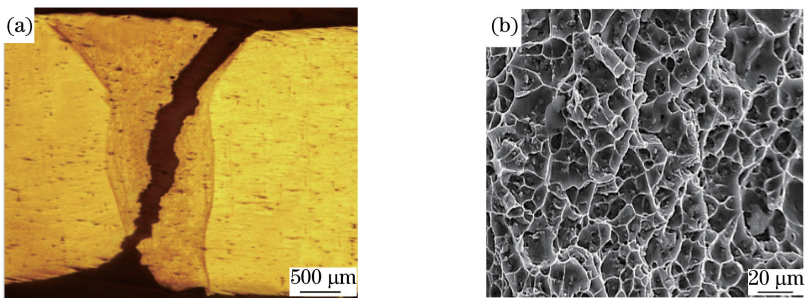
焊接接头拉伸断口。(a)断裂焊缝横截面;(b)断口形貌
